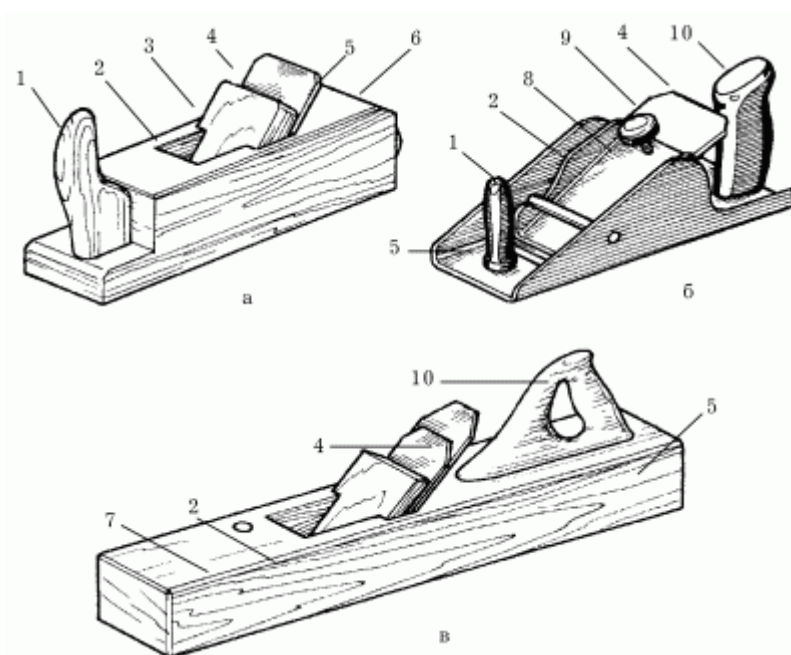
Элементы строгального инструмента: а – деревянный рубанок; б – металлический рубанок; в – фуганок: 1 – державка; 2 – леток; 3 – клин; 4 – нож; 5 – корпус; 6 – упор; 7 – пробка; 8 – прижим; 9 – винт; 10 – ручка.
